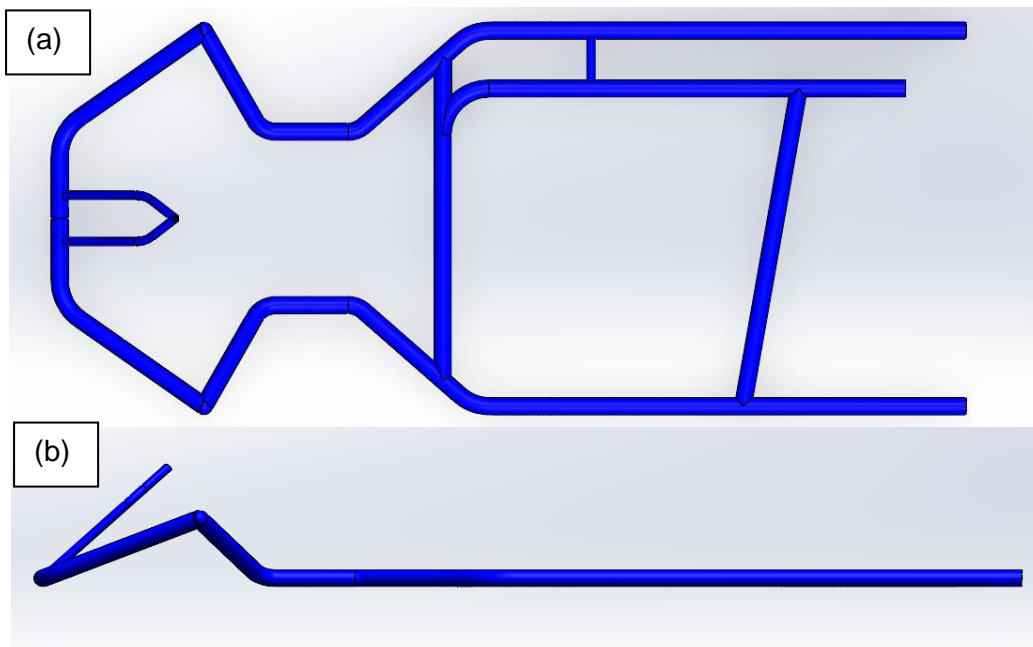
(a) Bastidor Planta; (b) Bastidor perfil
